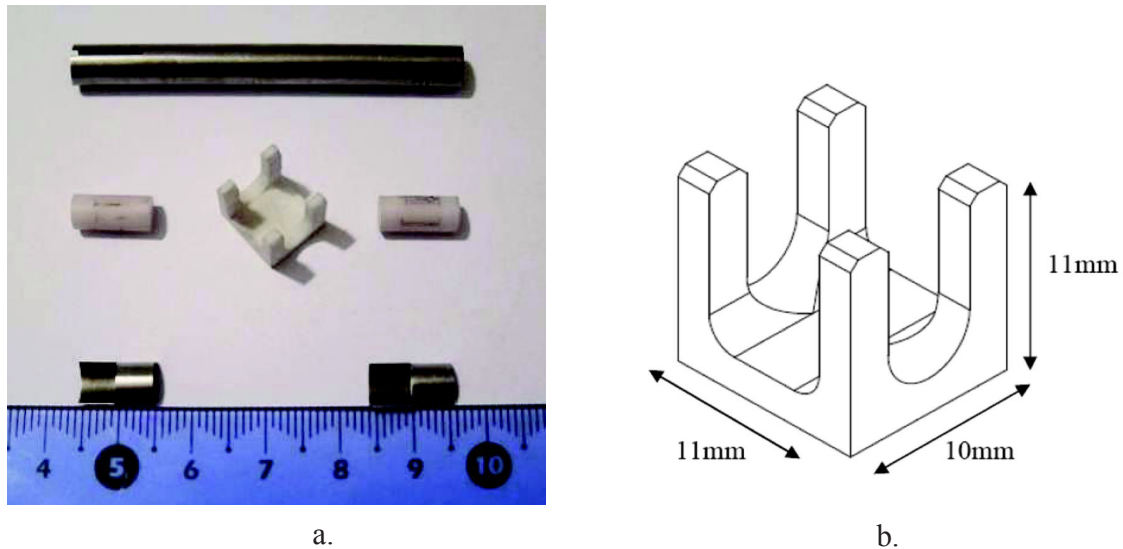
Détails du dispositif de montage des tubes; a. Les demi-tubes et les pièces du dispositif de montage en alumine; b. Géométrie de la pièce de support.
